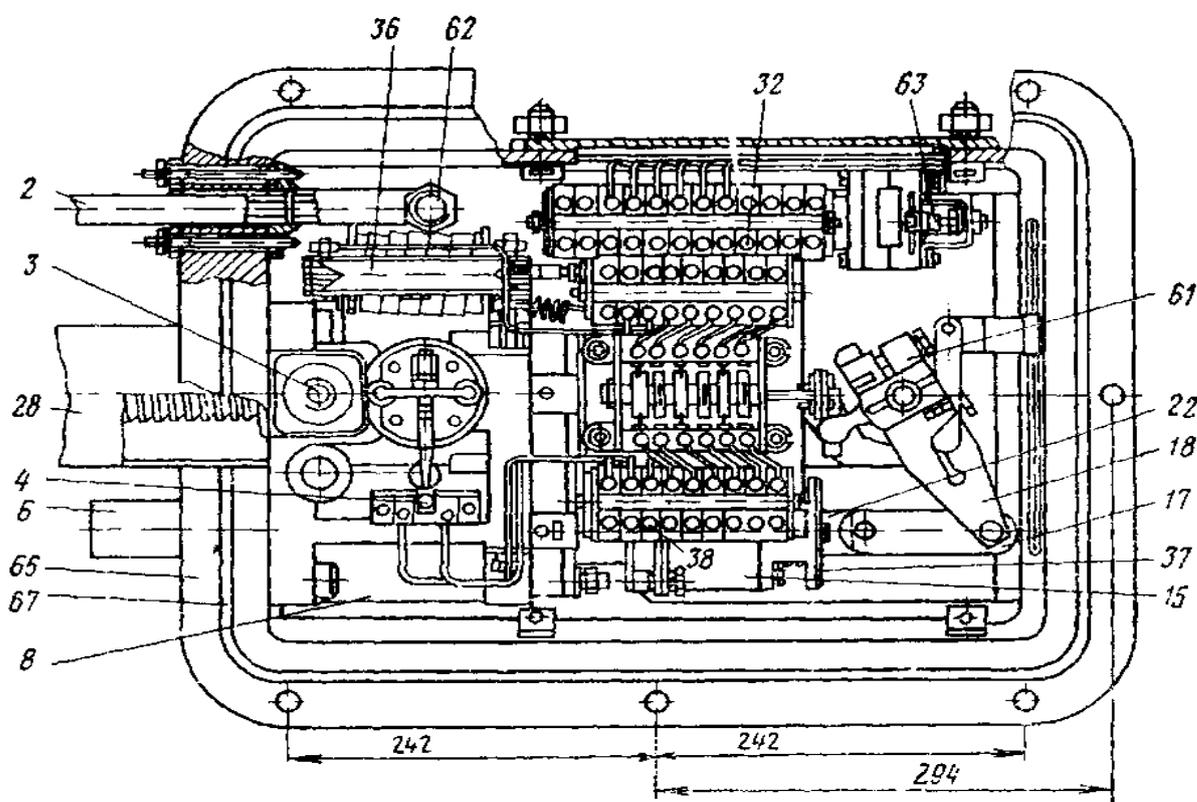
Корпус выключателя ВОВ 25-4М (вид снизу)
